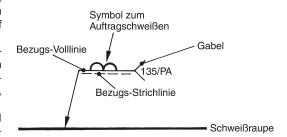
Darstellung der Auftragschweißung in der Zeichnung
